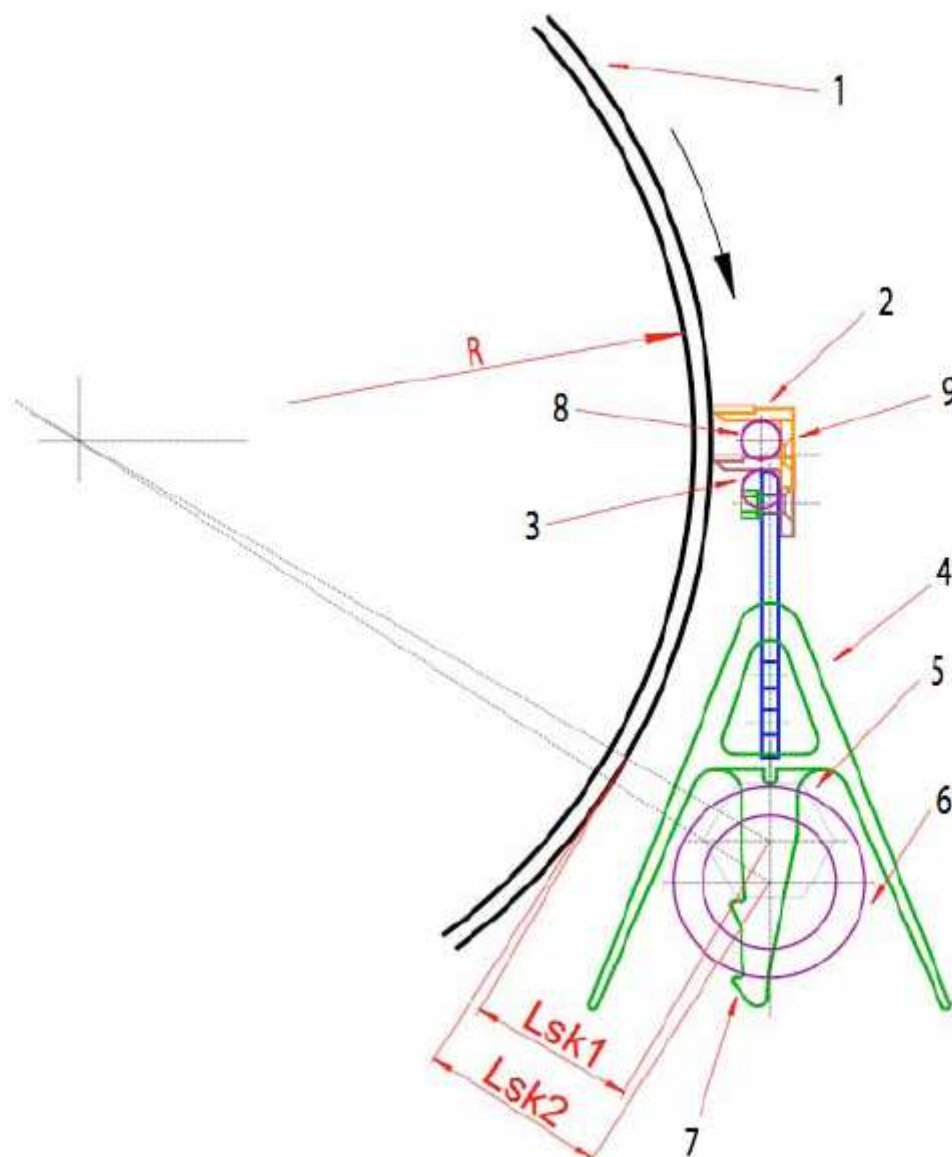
Vzájemná poloha shazovacího bubnu a stíracího segmentu typu 18
